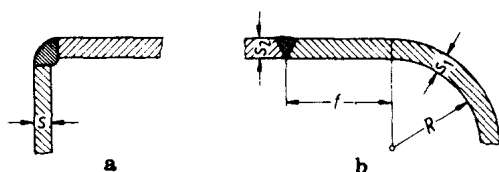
角结构 a. 角接焊缝; b. 预变形零件, 例如容器封头的转角处结构
